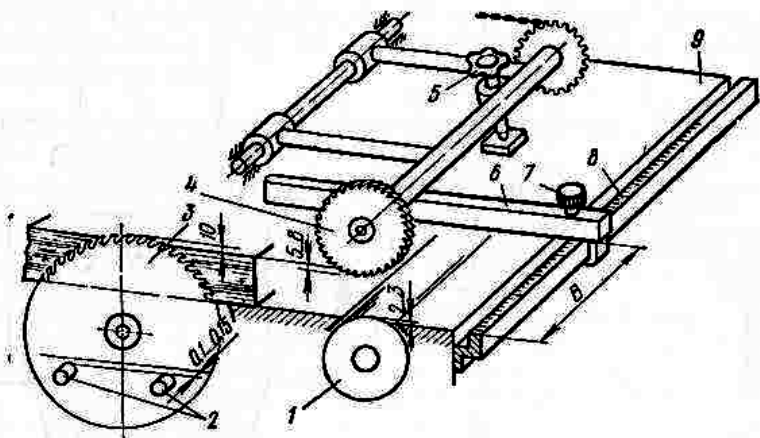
Настройка круглопильного станка с роликодисковой подачей:
